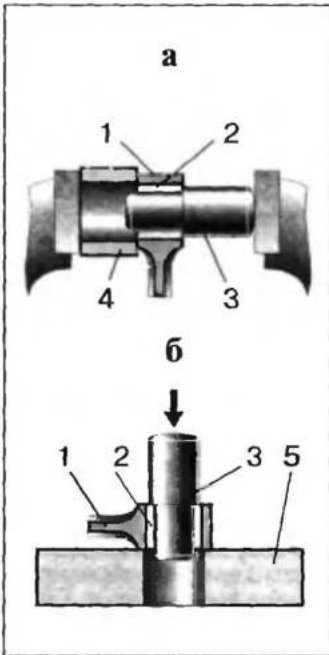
Выпрессовка втулок верхней головки шатуна: а — в тисках; б — ударным способом; 1 — шатун; 2 — втулка шатуна; 3 — технологический палец (выколота); 4 — технологическая втулка; 5 — плита
